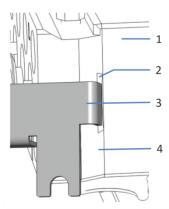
Entfernen der Hinterspülplatte mit dem Abstandswerkzeug
